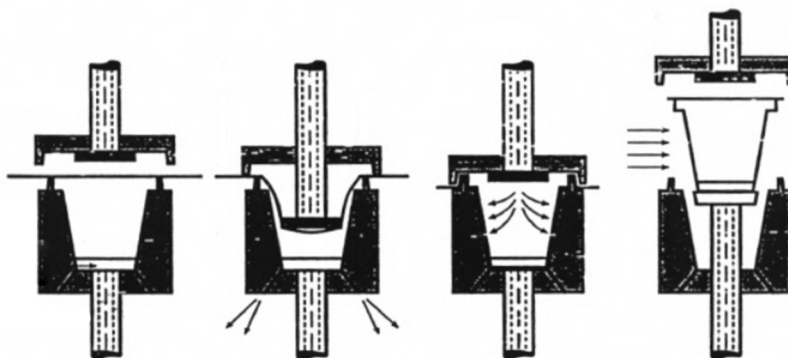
Termo Moldagem, (Giovannetti, 1995)
